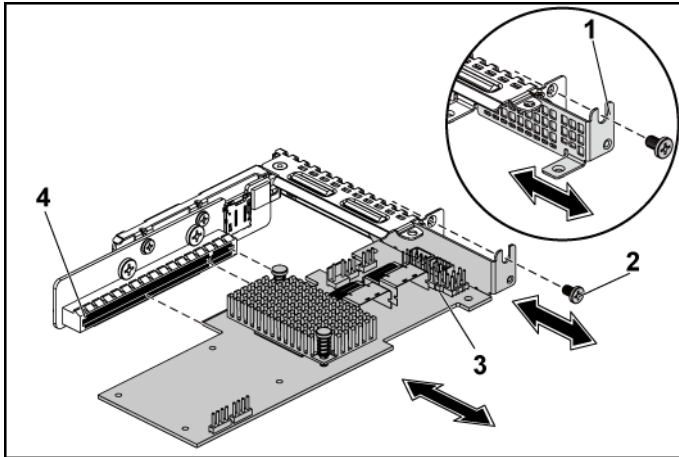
Retrait de l'assemblage de la carte LSI 9265-8i
